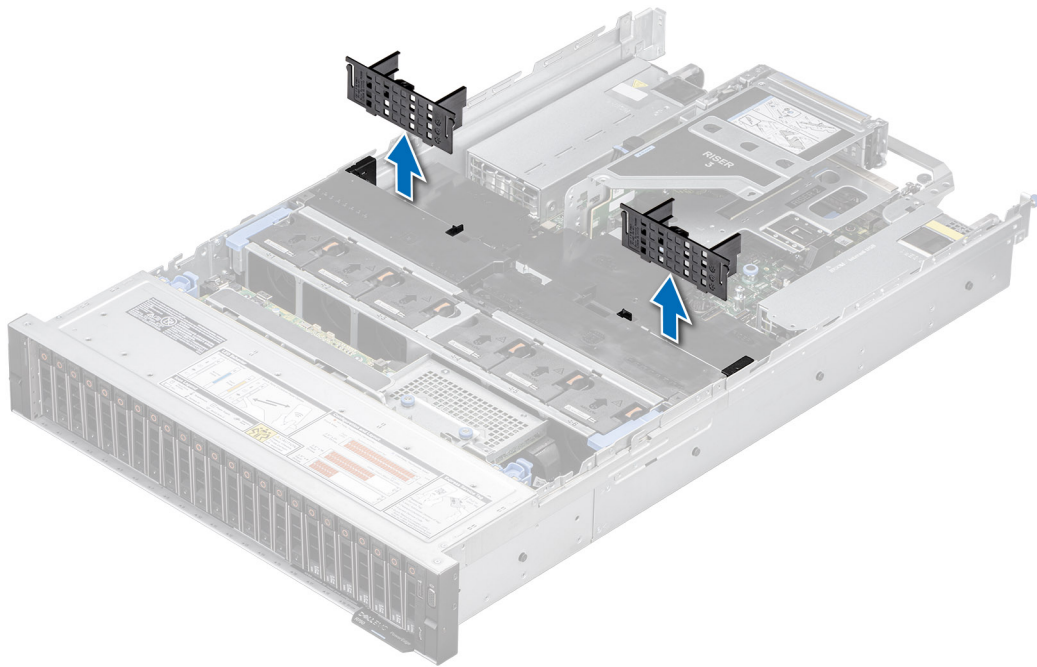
Extracción de la cubierta de relleno de la GPU
